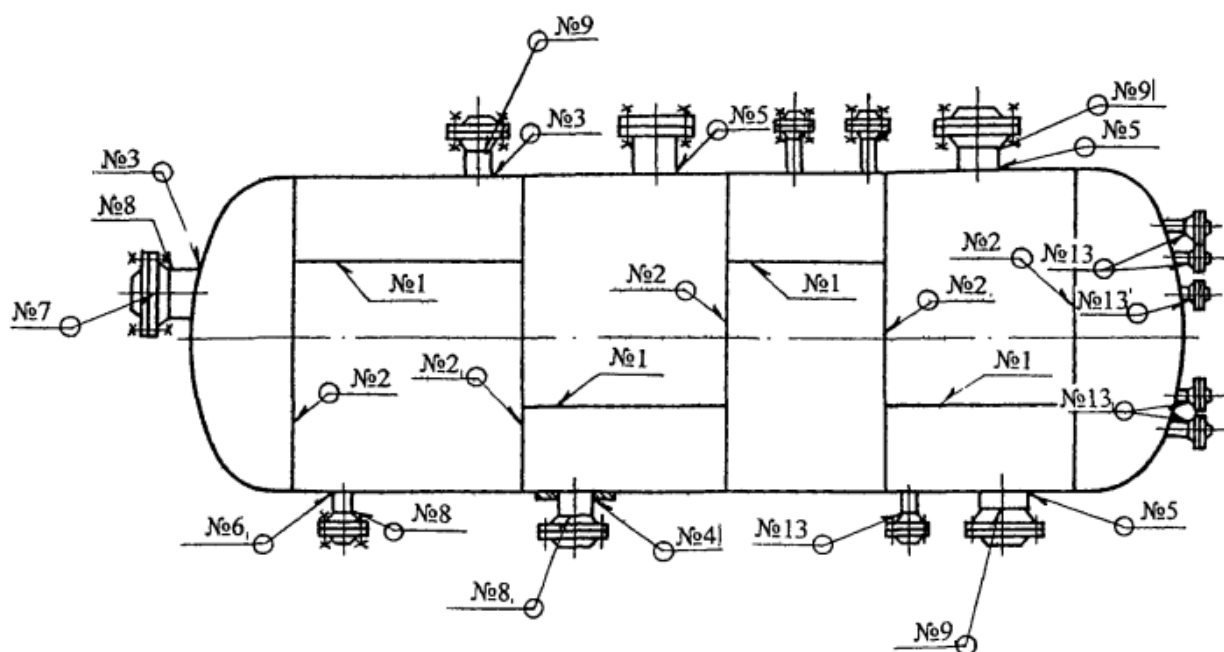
Карта контроля сварных соединений
